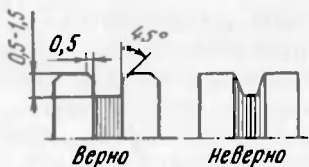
Размеры обработки пластин и выборки межпластинной изоляции при продороживании коллектора
